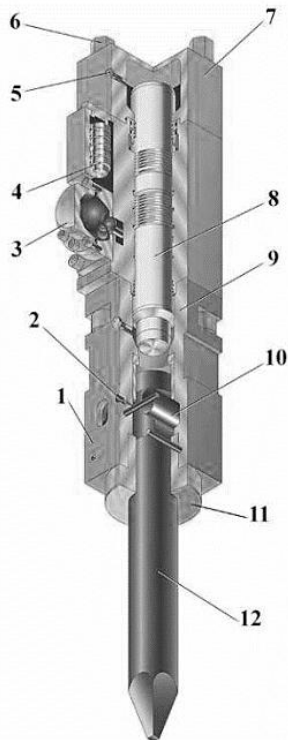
Пристрій поршневого гідромолота: 1 – нижній корпус; 2 – маслянка; 3 – гідроаккумулятор; 4 – гідророзподільник; 5 – клапан для заправлення азотом; 6 – стяжний болт (шпилька); 7 – кришка циліндра; 8 – поршень; 9 – робочий циліндр; 10 – палець; 11 – нижня втулка; 12 – робочий інструмент (піка) [2]
